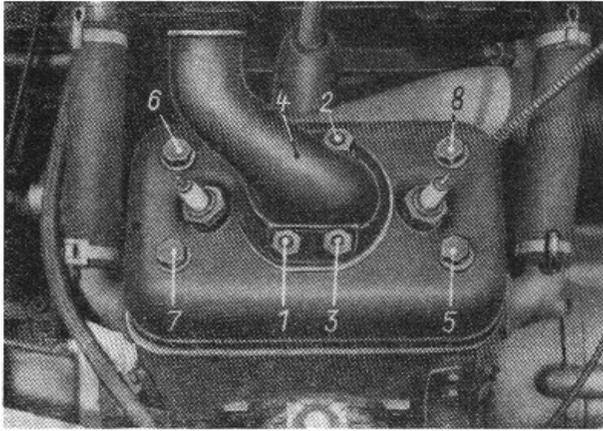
Reihenfolge für das Anziehen der Zylinderkopfschrauben
